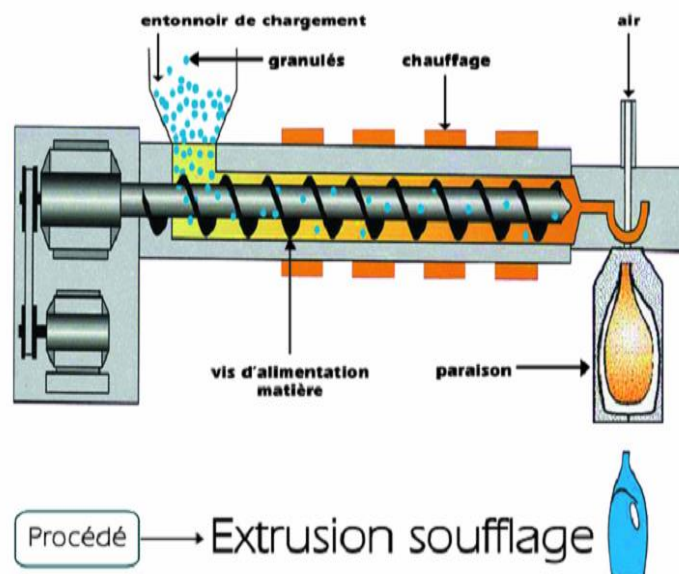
Exemple de procédé d'extrusion-soufflage
